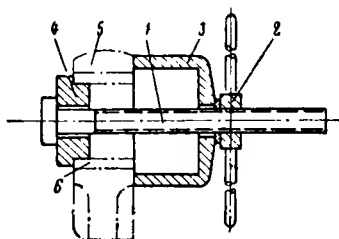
Приспособление для выпрессовки и запрессовки втулок шатунов компрессоров: 1 — болт; 2 — гайки с рычагами; 3 и 4 — упорные шайбы; 5 — шатун; 6 — втулка
